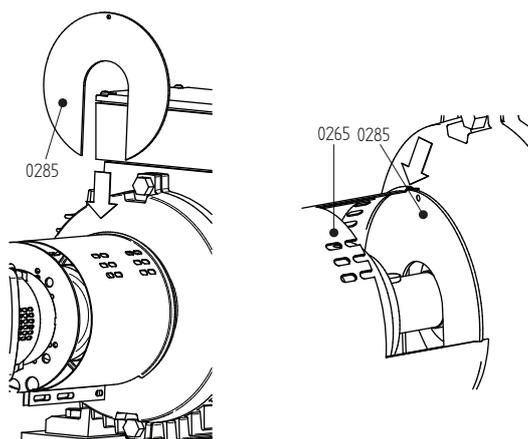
Montare lo scudo d'assemblaggio a lato del motore.
